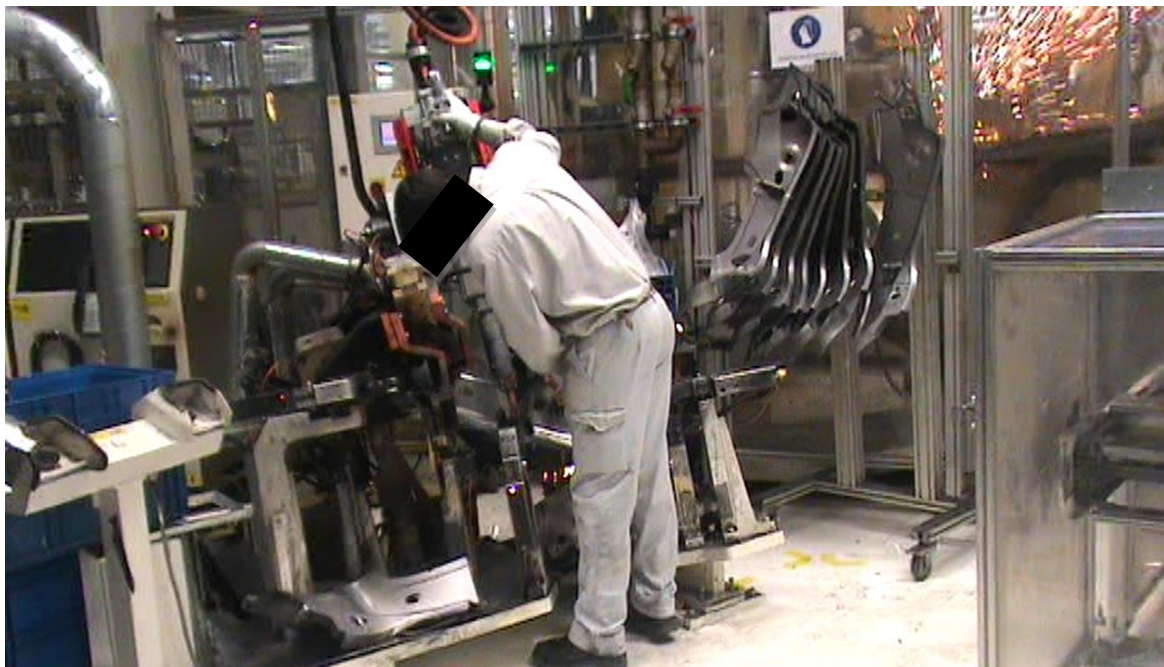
Situação K : Manipulação da pistola de soldadura
